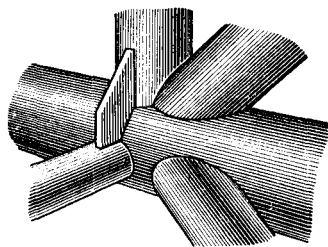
Соединение труб, подготовленное к сварке
